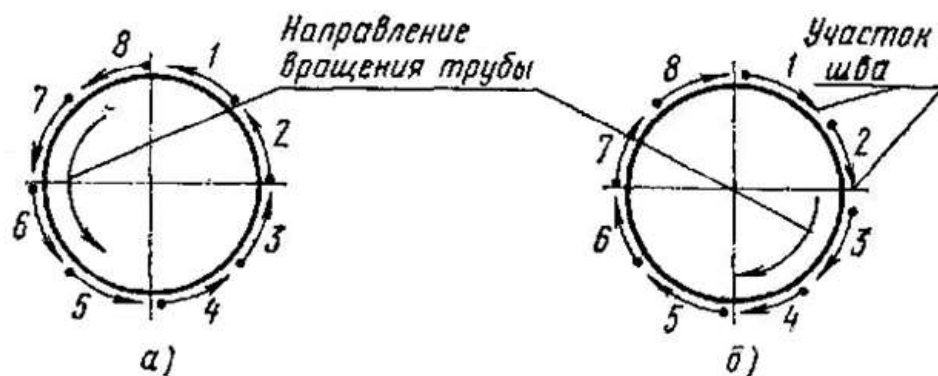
Схема сварки стыка труб большого диаметра:
